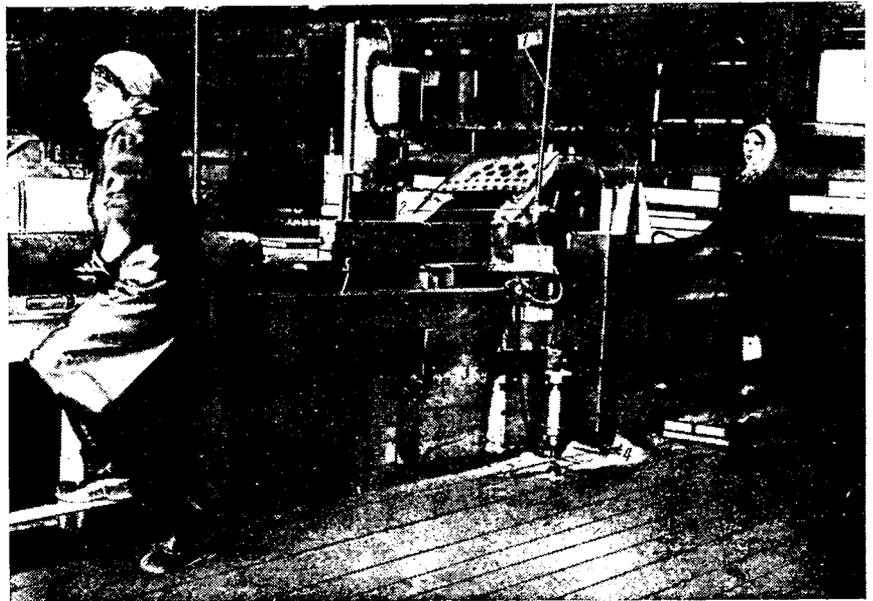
Общий вид стола торцовочного станка с оборудованием для пневматического подъема пилы:
